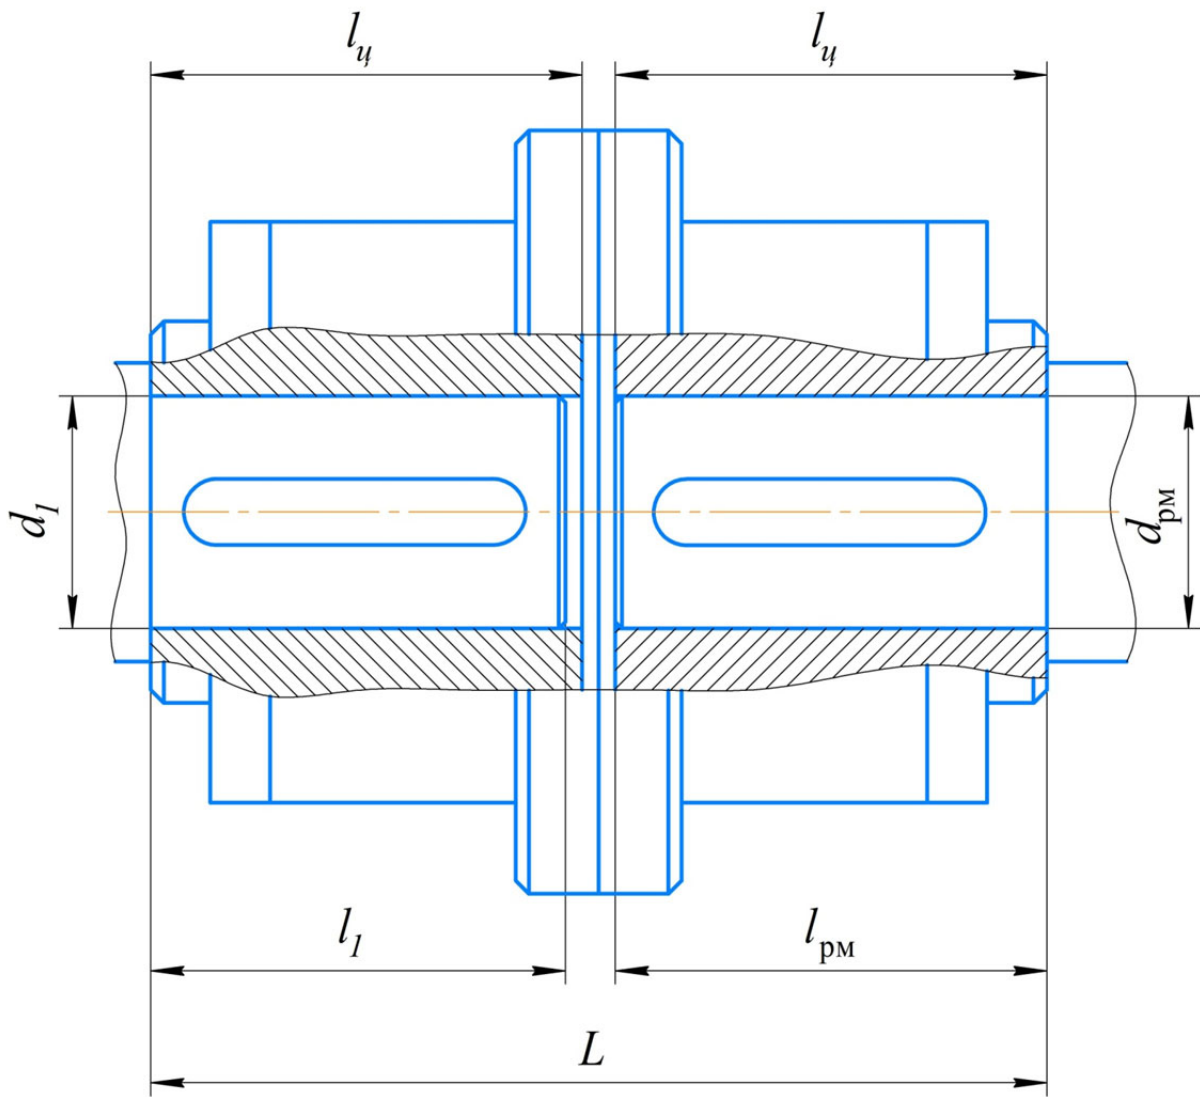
Установка зубчатой муфты на цилиндрических концах валов привода:
